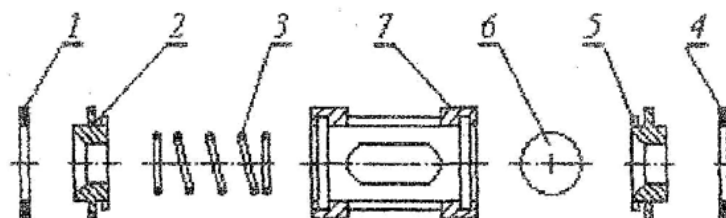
Розташування деталей в гільзі клапана: (розбирання гільзи клапана вести в черговості за номерами позицій на кресленні) 1 – прокладка; 2 – сідло; 3 – пружина; 4 – прокладка; 5 – сідло; 6 – кулька; 7 – корпус гільзи
